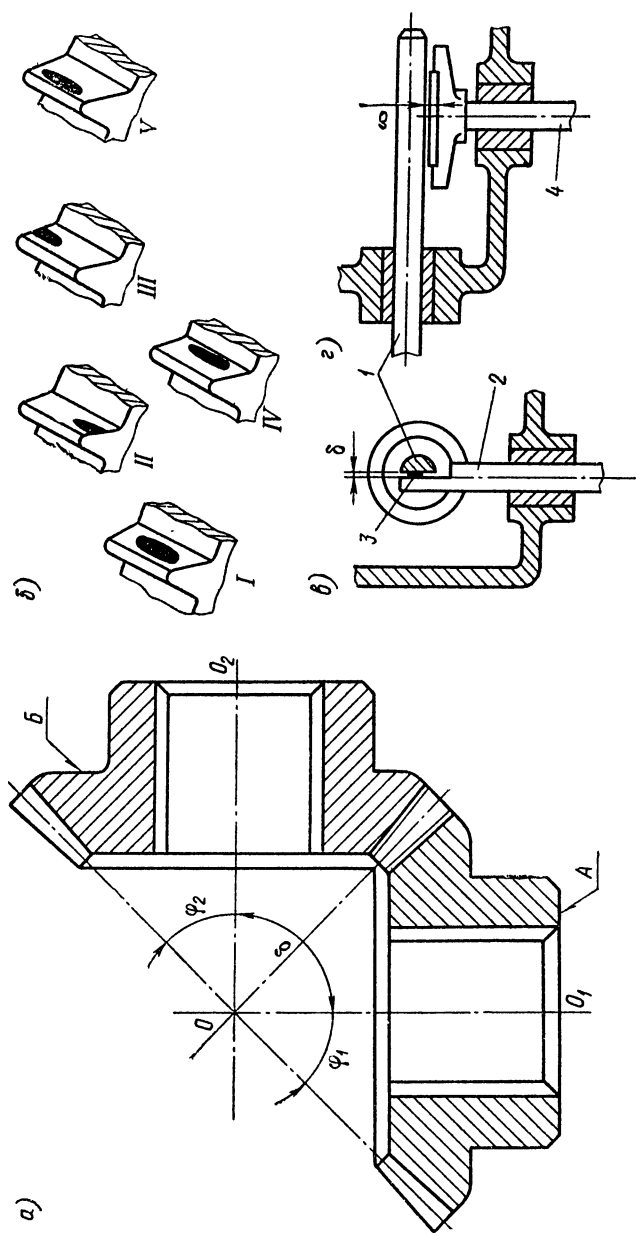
Коническая зубчатая передача: *а* — элементы зацепления; *б* — контроль качества зацепления; *в*, *г* — контроль расположения осей в корпусе
